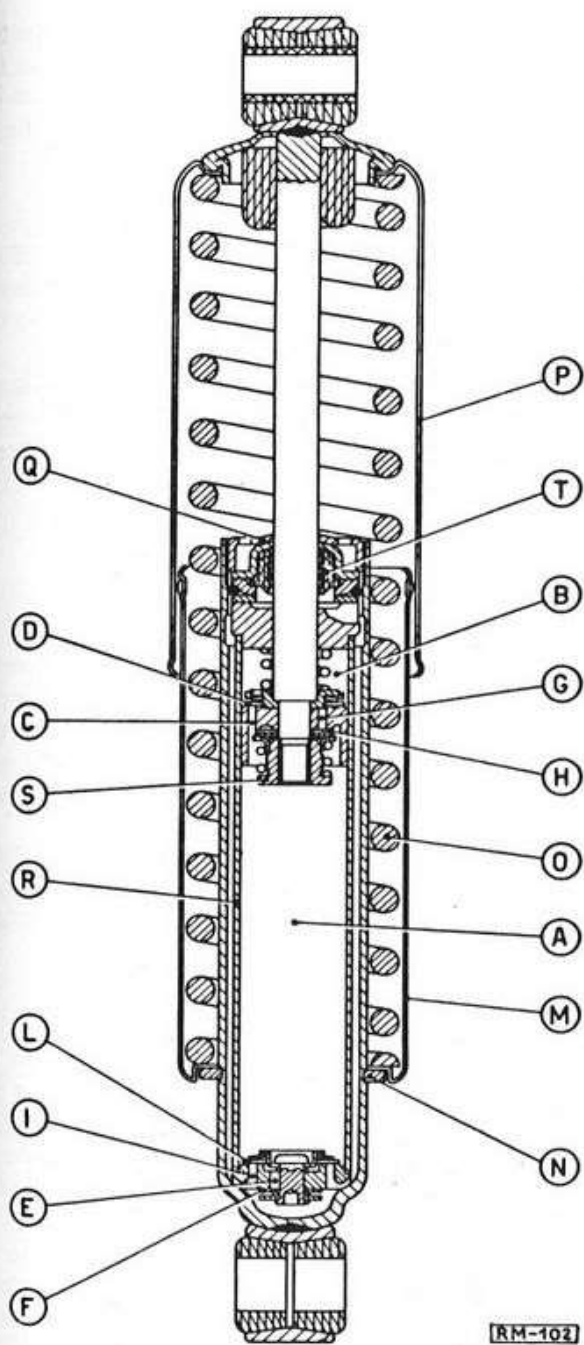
Sezione di un elemento telescopico della sospensione posteriore.
